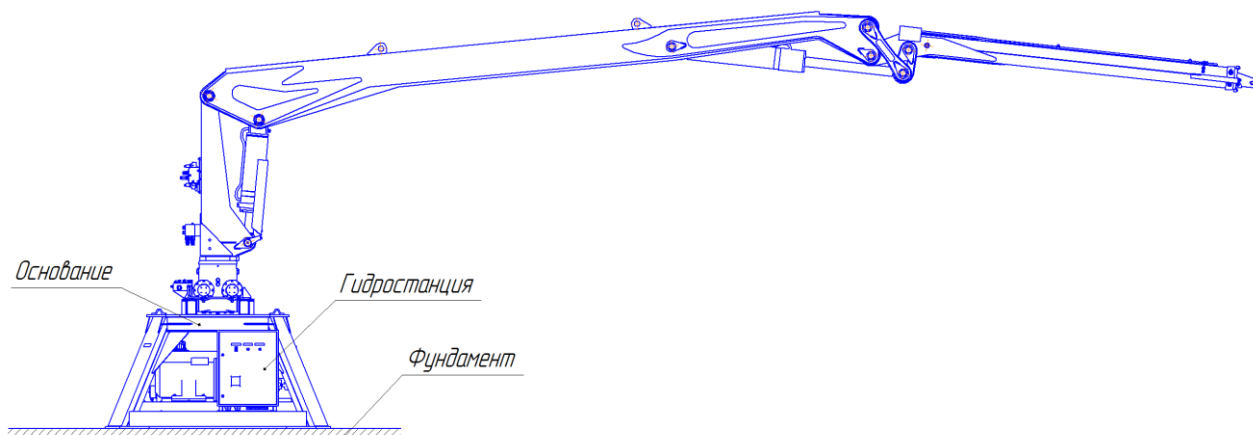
Монтаж манипулятора на опору и фундамент
